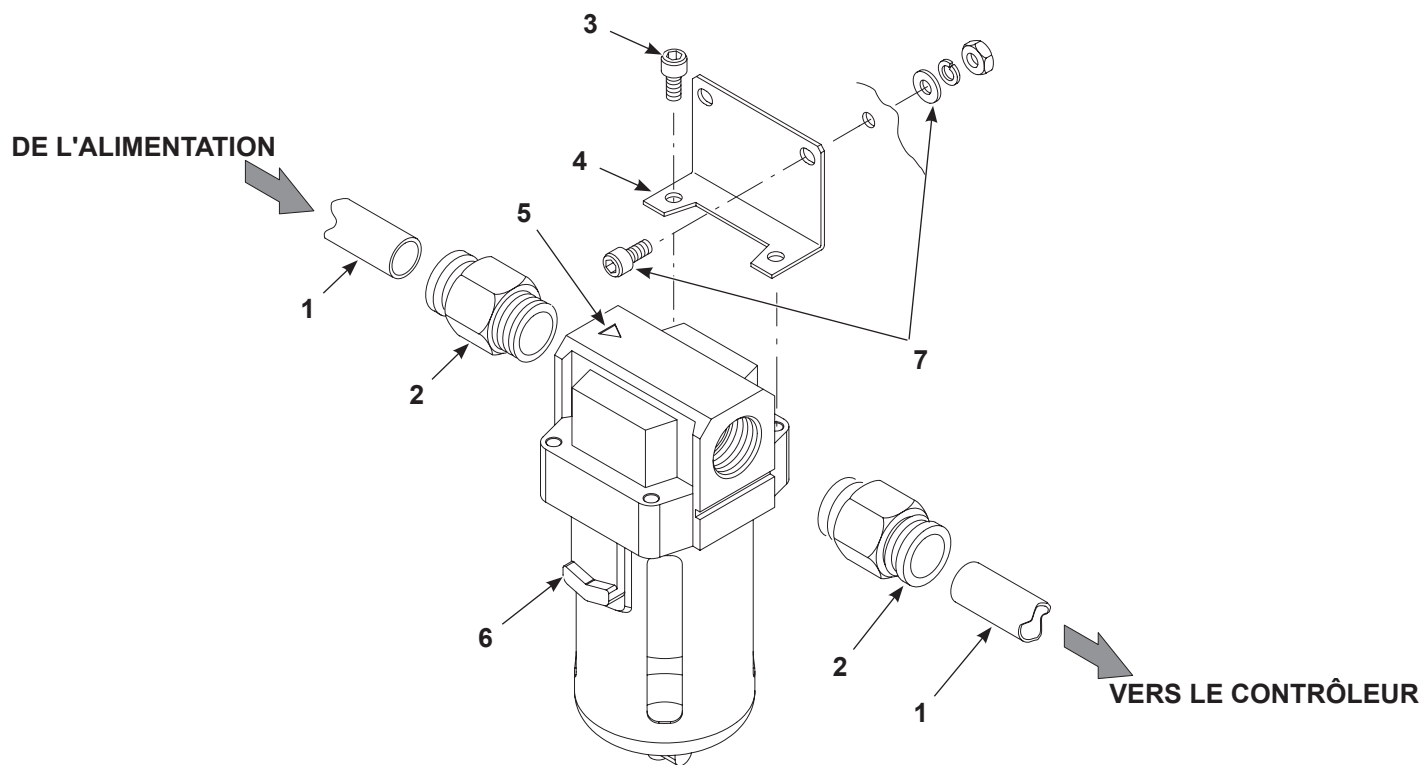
Installation du filtre à air – Systèmes à montage mural et sur rail
